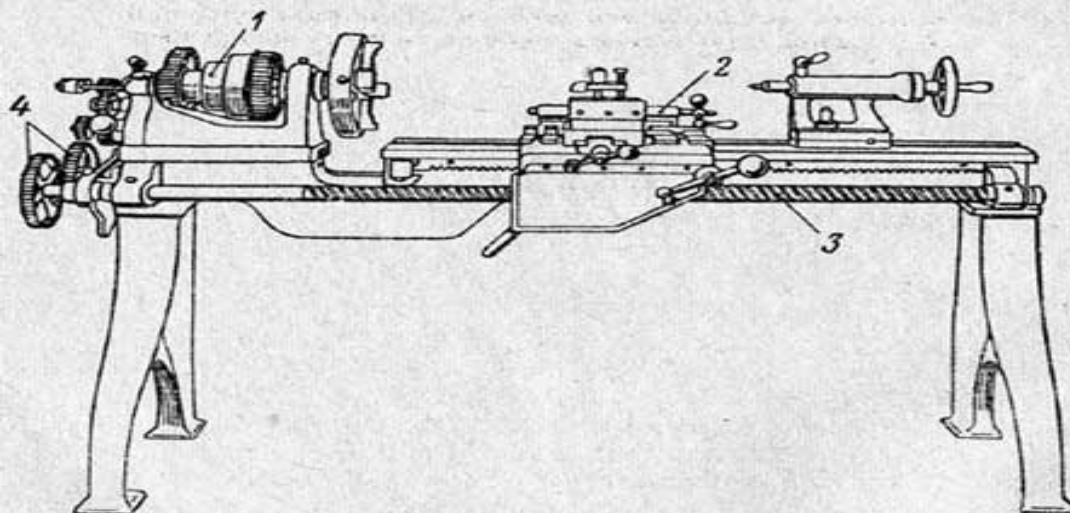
Токарный станок середины XIX века со ступенчатым шкивом
